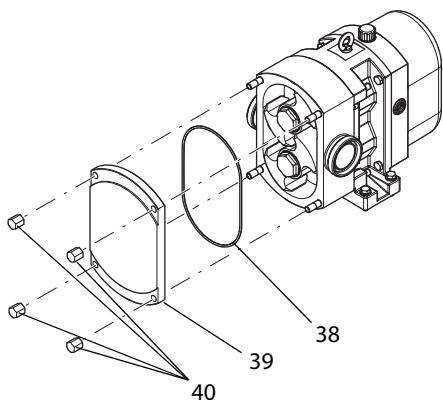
Закрывание крышки корпуса на примере насоса ε: 100
